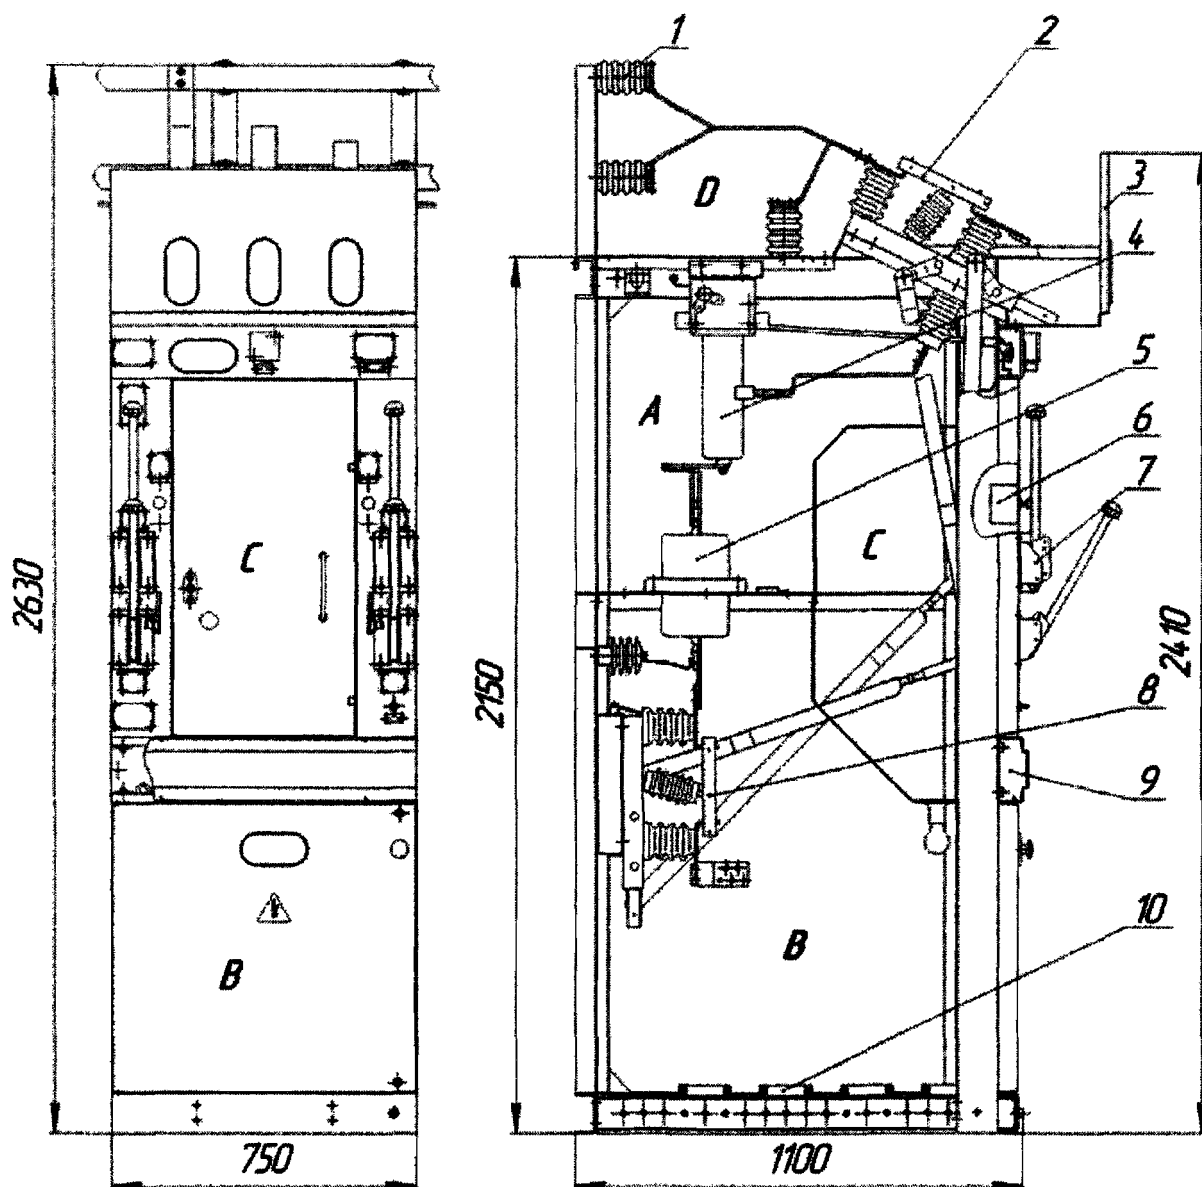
Габаритные, установочные и присоединительные размеры камеры КСО - 204
